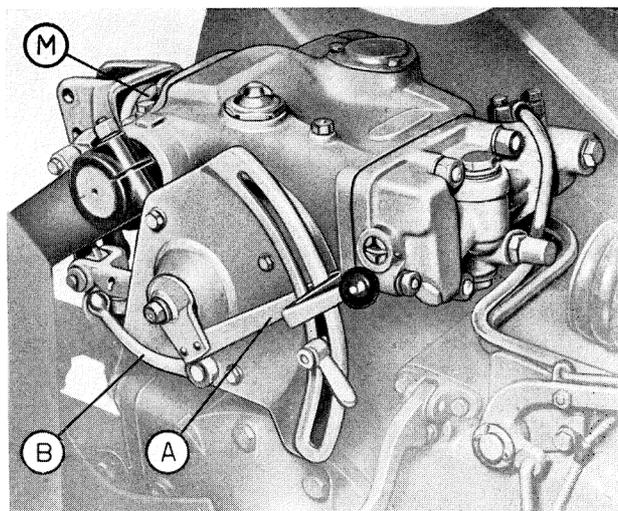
Relevage hydraulique monté sur le tracteur.
